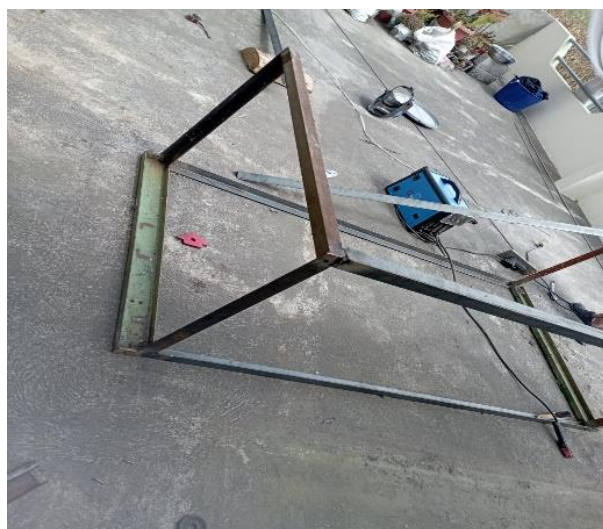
Ensamble y soldadura de la estructura.
